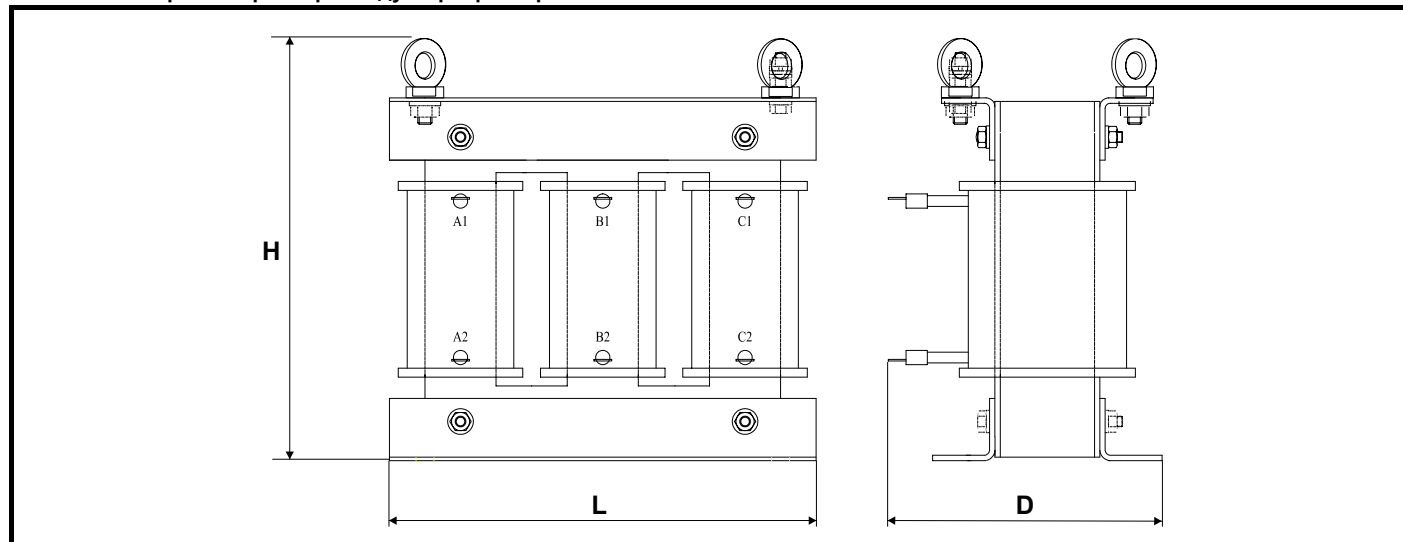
Габаритные размеры индуктора фильтра частоты ШИМ типа 3
